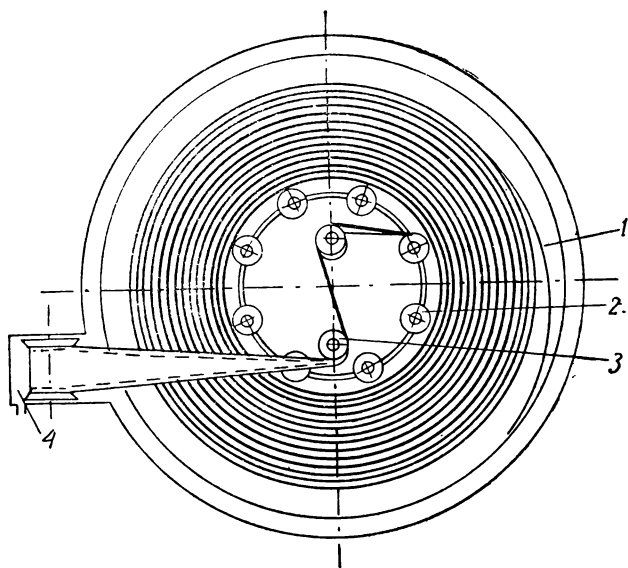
Схема прохождения фильма в разматывателе, в котором рулон размещается на неподвижном диске (вид сверху):
